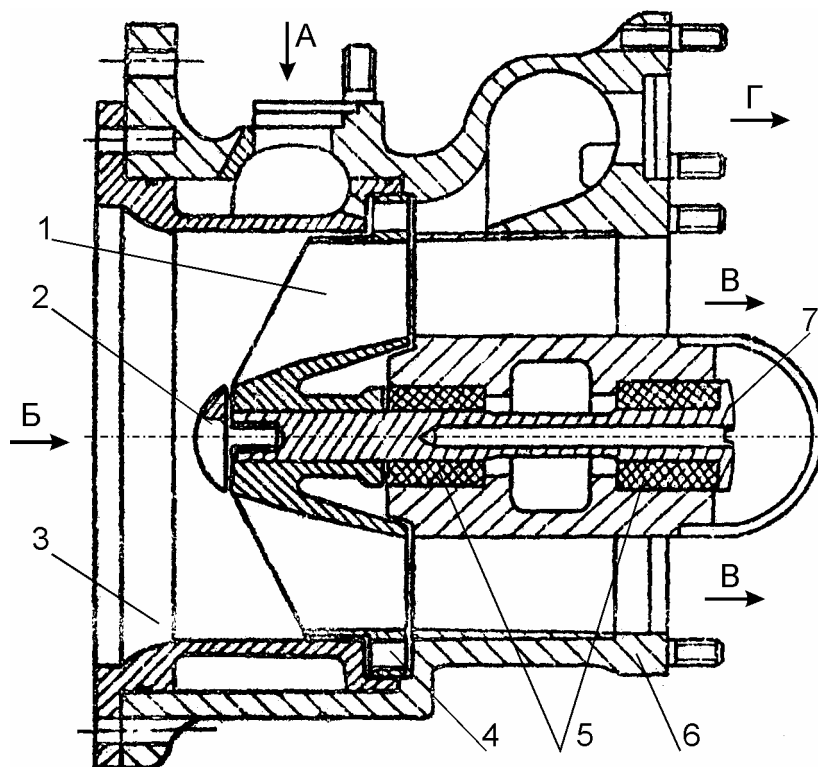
Осьовий гідротурбопривідний насос без змішування (ГТН-7): 1 — робоче колесо; 2 — фіксувальний гвинт; 3 — напрямний апарат; 4 — турбіна; 5 — підшипники; 6 — корпус; 7 — вісь; А — вхід активного палива; Б — вхід палива з бака; В — вихід палива, що подається; Г — вихід активного палива
